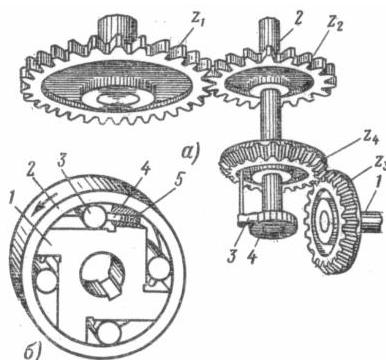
Муфты обгона: а – храпового типа; б – роликового типа
